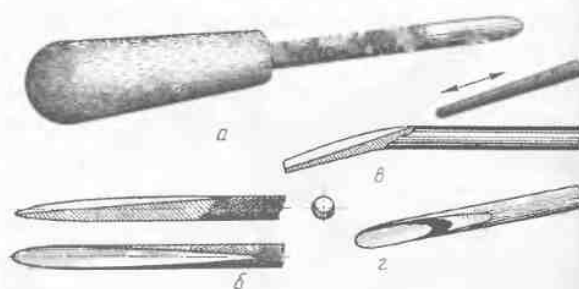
Резец: а — изготовленный из круглого напильника — вид на стержень с обратной стороны канавки; б — чертеж стержня полукруглого резца; в — вытачивание канавки на изогнутом стержне; г — изготовленный из круглого стержня сверлением канала с торца
